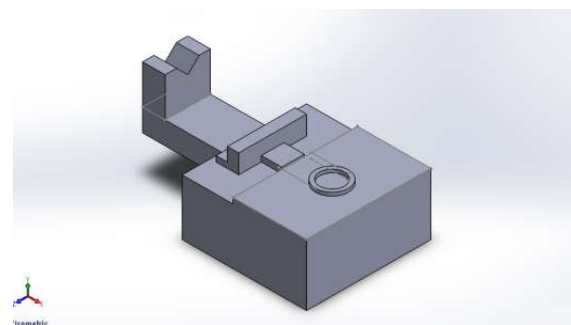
Fixture proses *flange install* sebelum perbaikan.
